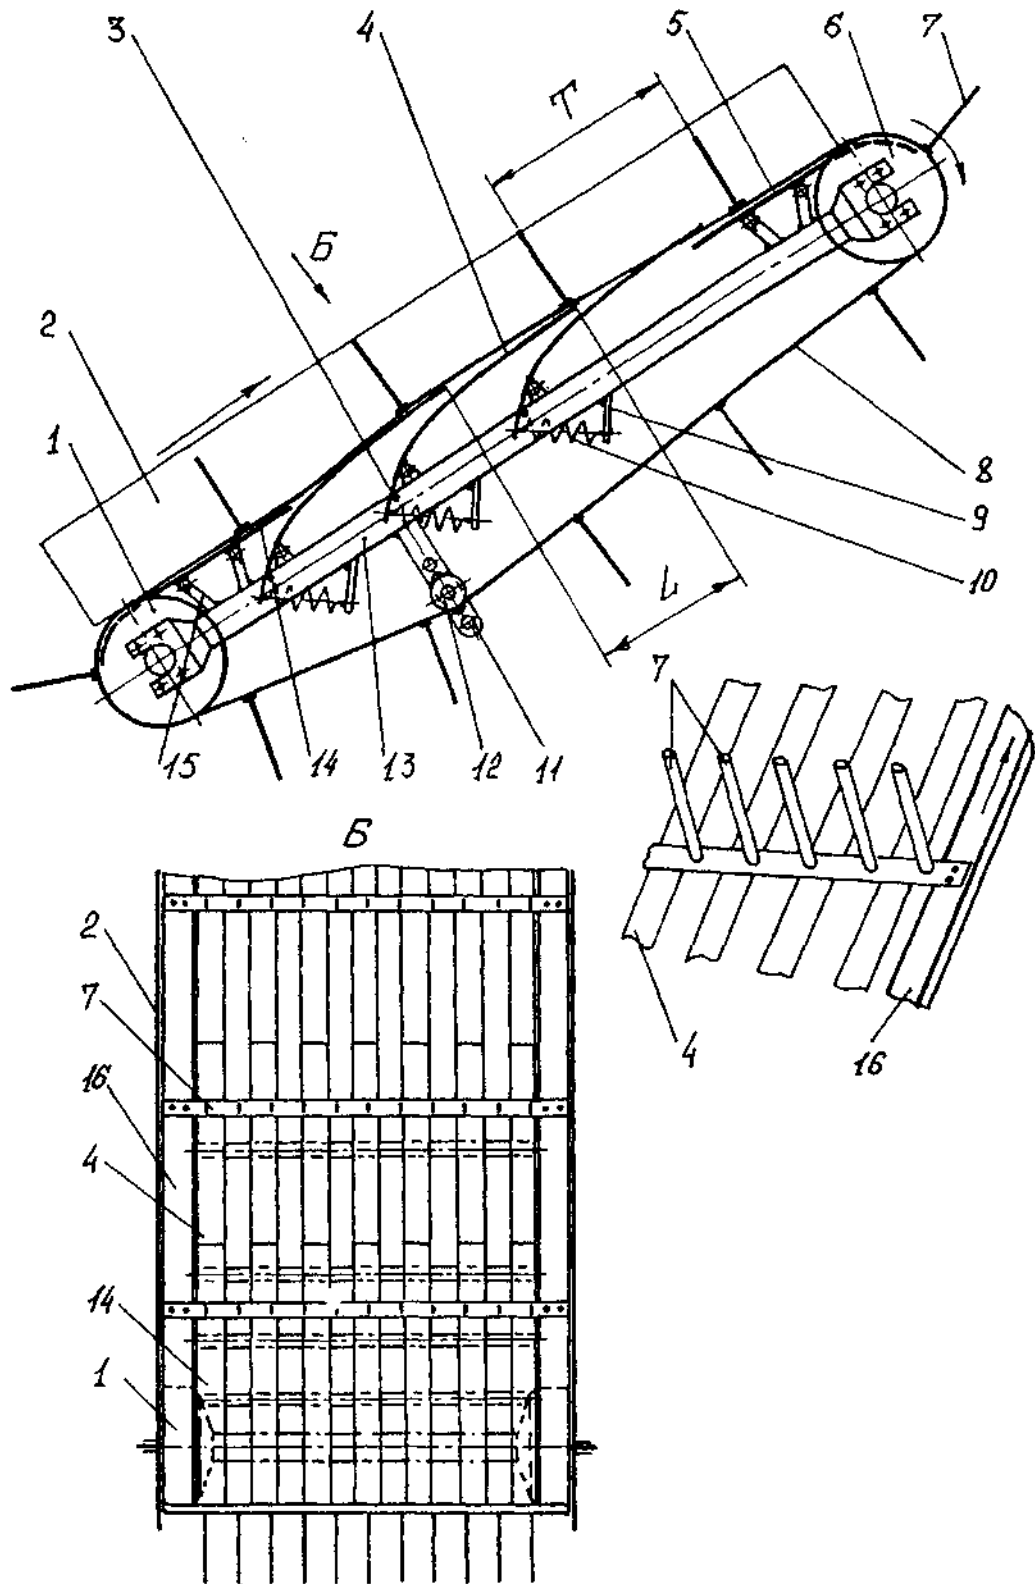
Конструктивно-технологічна схема скребкового доочисного транспортера
